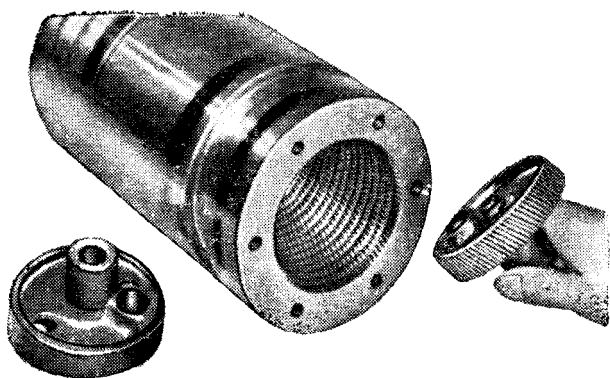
Протяжка-труба для протягивания зубчатых колес с винтовым зубом
